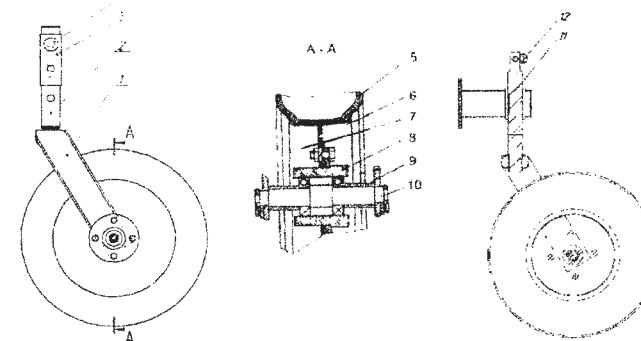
Опорный каток 1 - вилка; 2 - ползун; 3 - опора; 4 - палец; 5 - шина; 6, 7 - обод; 8 - ступица; 9 - втулка распорная; 10 - ось; 11 - винт; 12 - ручка;
